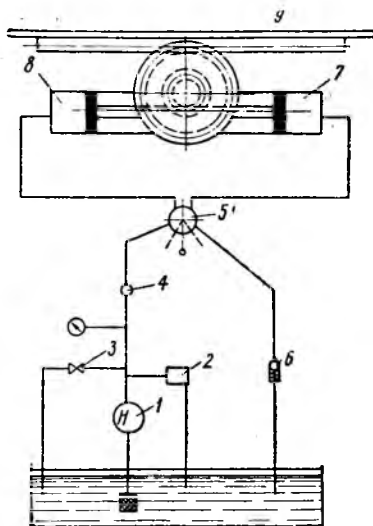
Усовершенствованная гидравлическая схема привода станка: 1 — насос Л1Ф-35; 2 — напорный золотник; 3 — двухходовой кран; 4 — золотник; 5 — четырехходовой кран; 6 — обратный клапан; 7, 8 — цилиндр; 9 — рабочий стол
